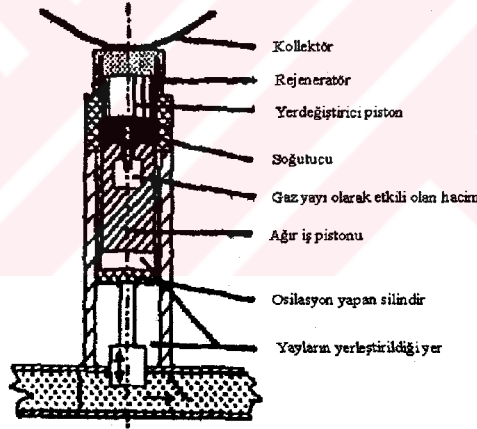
Membranlı serbest pistonlu Stirling Motoru
